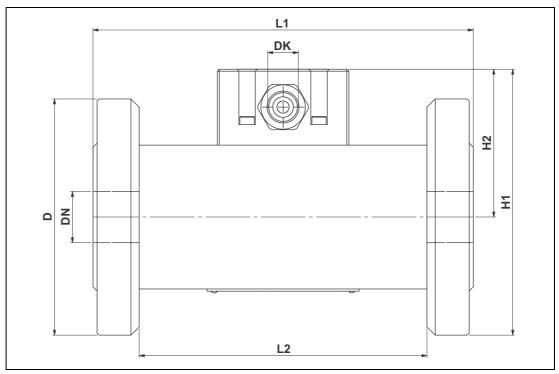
Maßzeichnung OME mit DIN-Flansch
